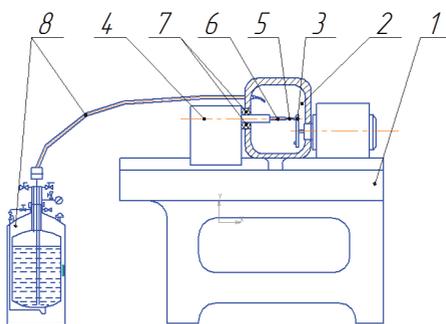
Схема установки: 1 - рама; 2 - герметичный корпус ;
